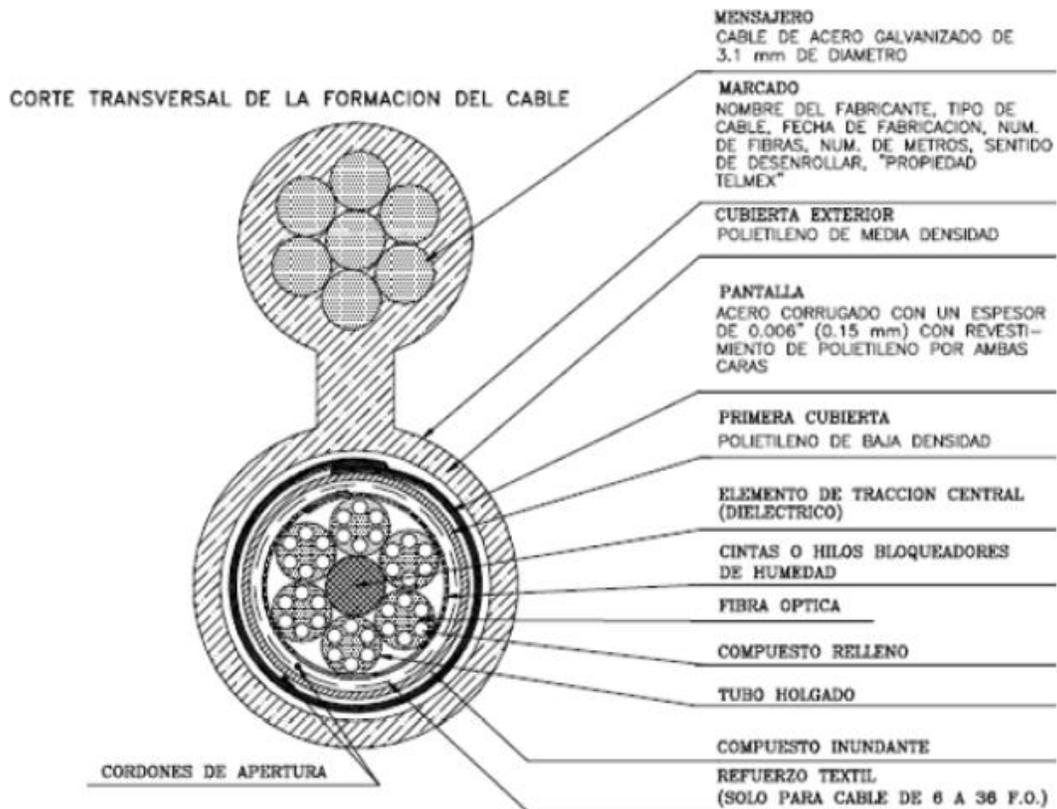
Descripción técnica del cable de Fibra Óptica TM-6N
